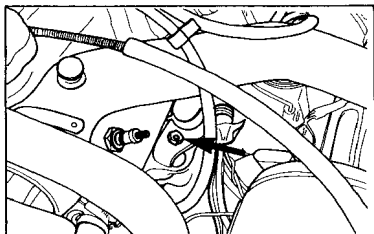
Гайка прижимной планки корпуса распределителя, имеющего контактный прерыватель
